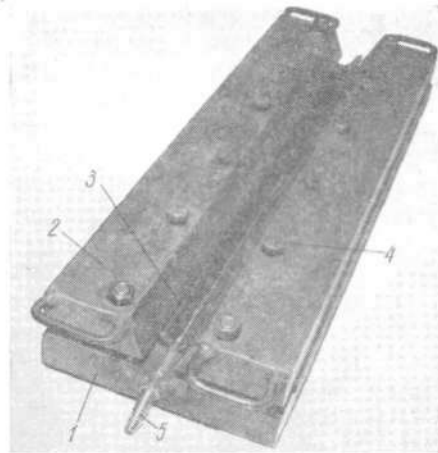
Зажимное приспособление для сборки плоских листовых конструкций.
